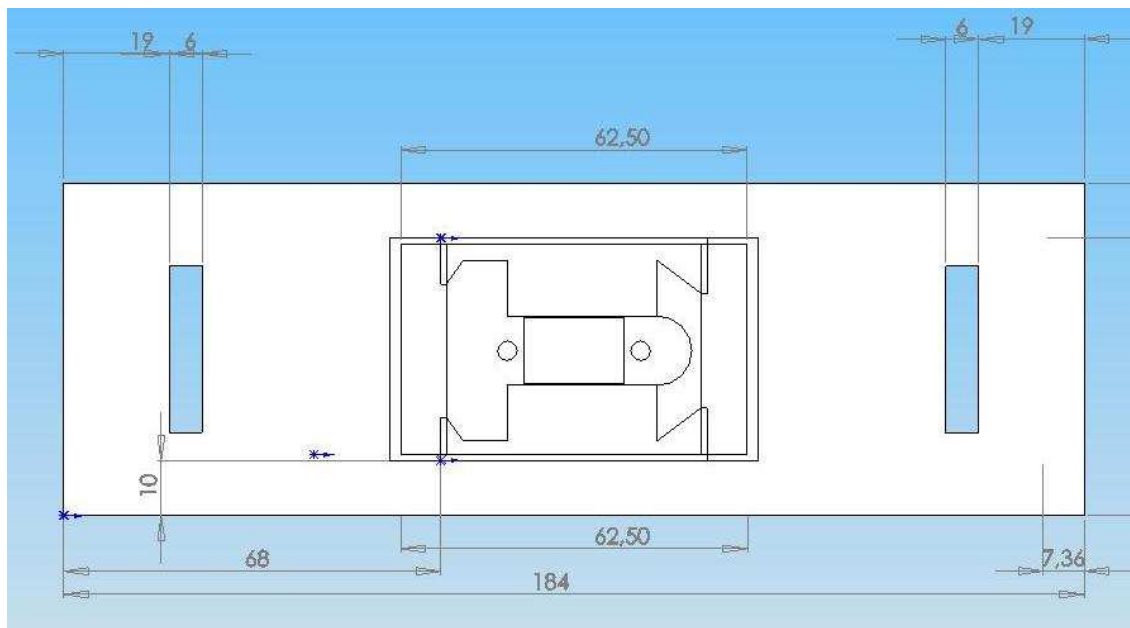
Dimensiones plancha de aluminio tubo corto.
